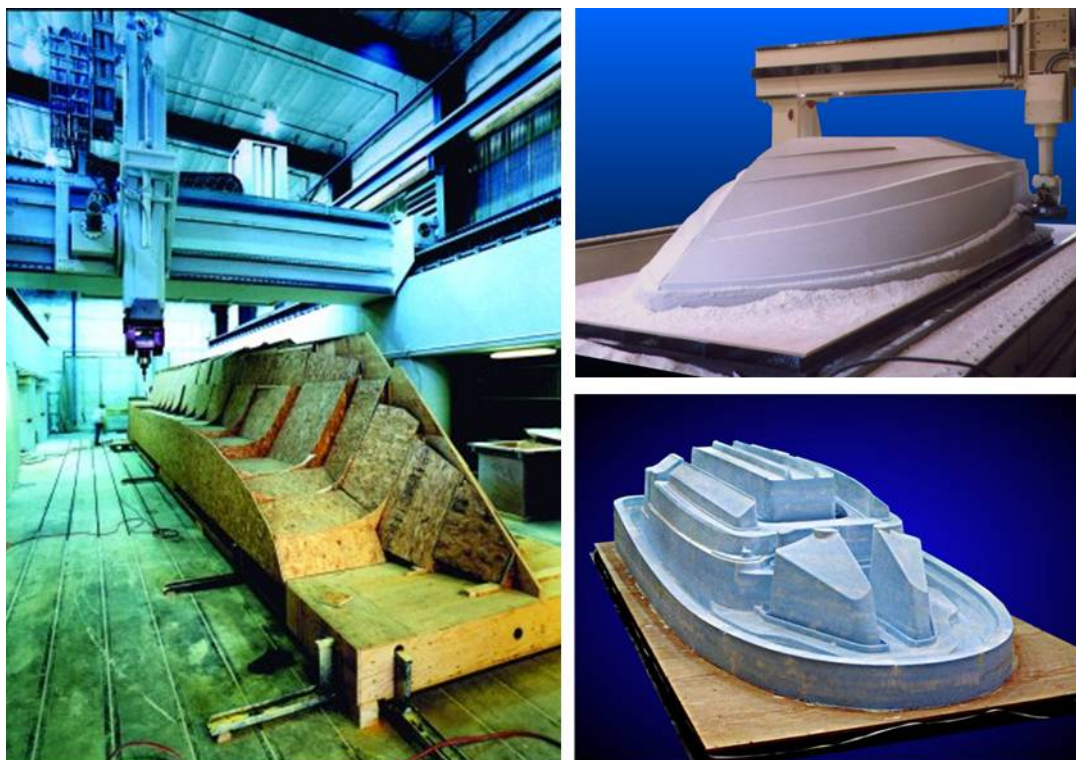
Exemplos de máquinas CNC para usinagem de embarcações
